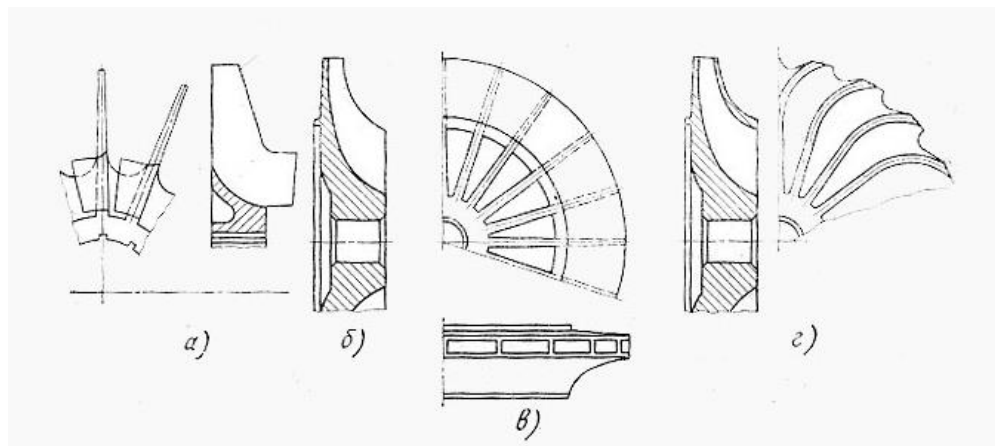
Односторонние колеса центробежных компрессоров:
